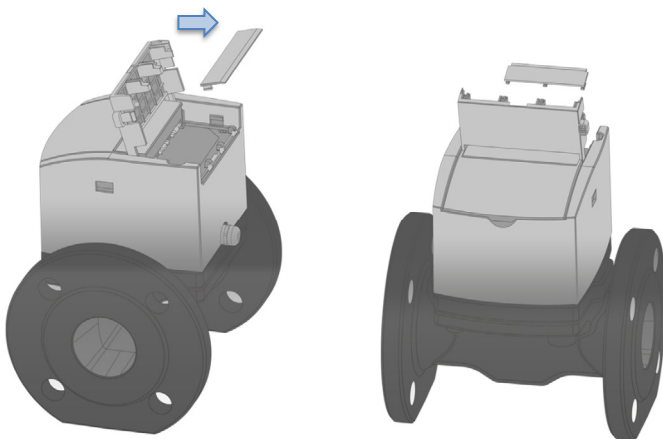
Remplacement du cache de protection en vue de l'ajout d'un nouveau module
